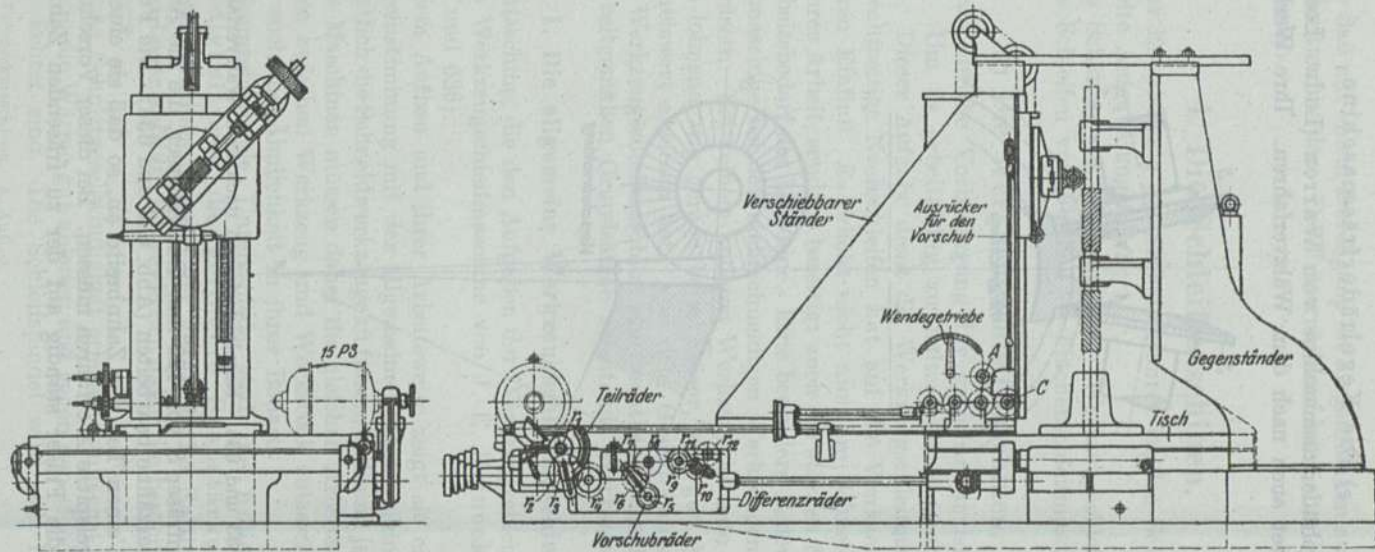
und 629. Schraubenräderfräsmaschine von J. E. Reinecker, A. G., Chemnitz.
